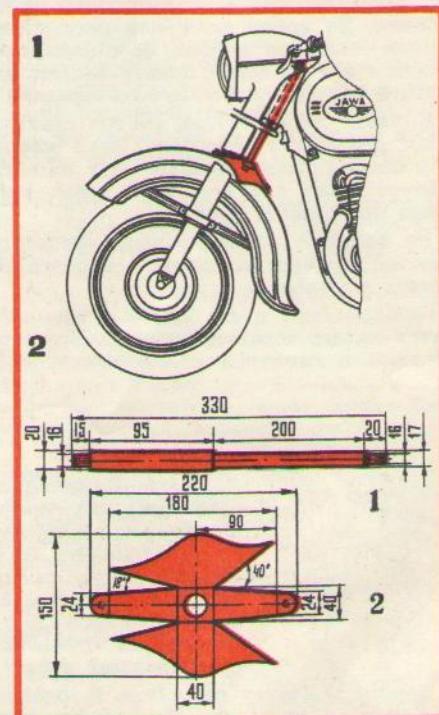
Крепление крыла переднего колеса «Явы-350».
